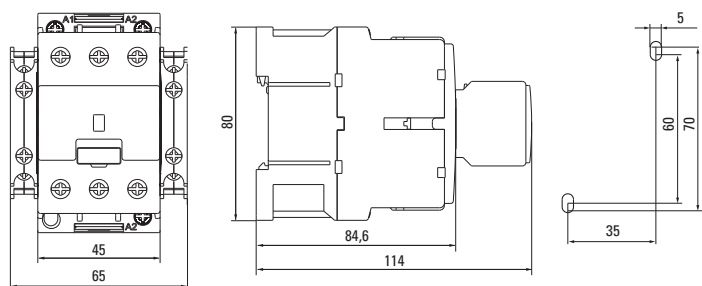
Габаритные и установочные размеры контакторов КМЗ 32А, КМЗ 38А
